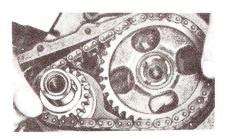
Desmontaje de Cadena y Engranaje de Sincronización. Típico
